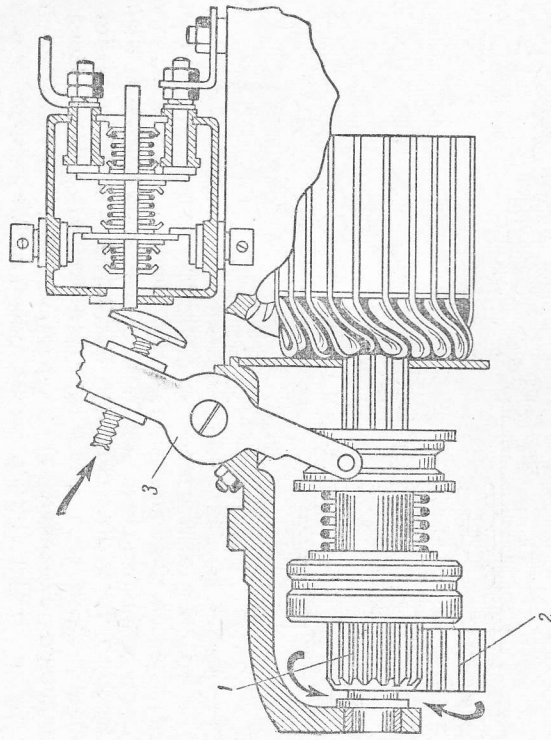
Схема расположения деталей включающего механизма при включении стартера:
